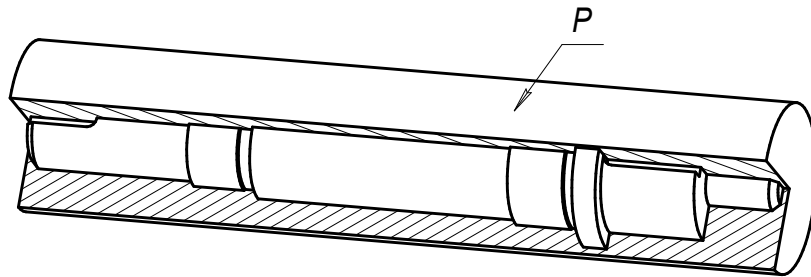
Конструкція заготовки для деталі вал 5В.17.008
